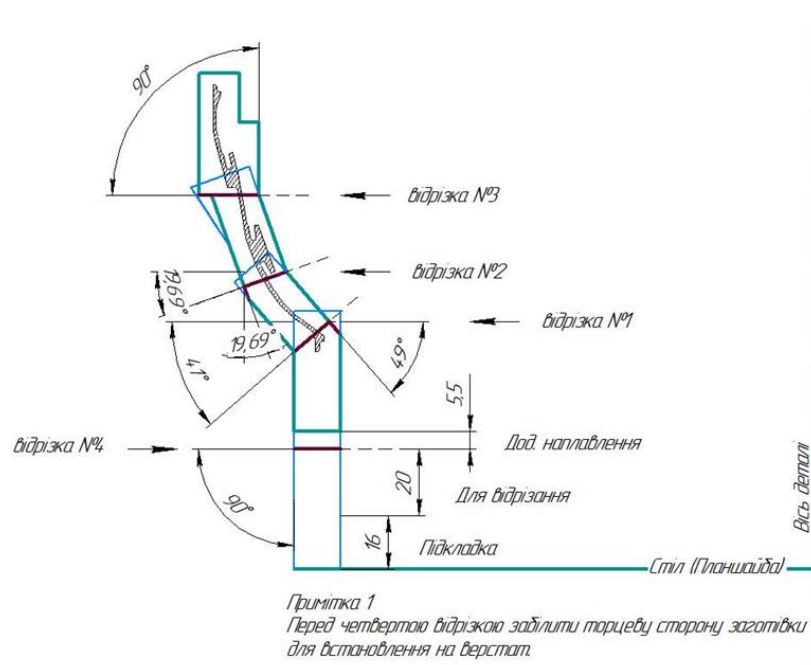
Креслення чотирьох токарних операцій наплавлення деталі
